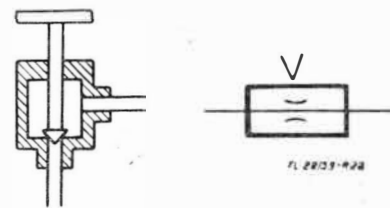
Zawór odcinający o jednokierunkowym działaniu
